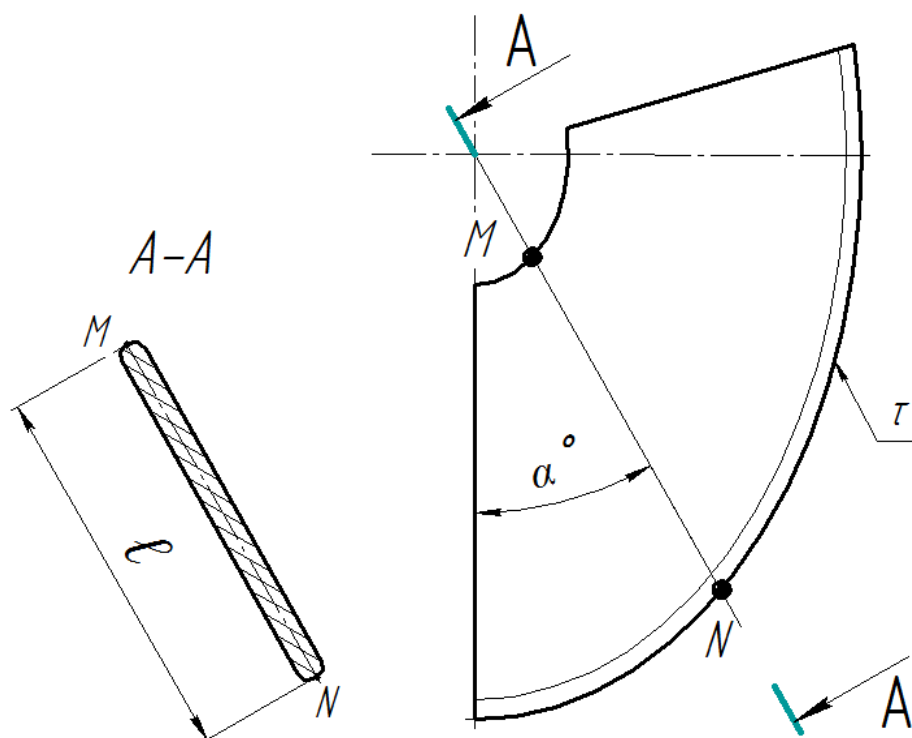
Чертеж лопасти вала дозаторного устройства
